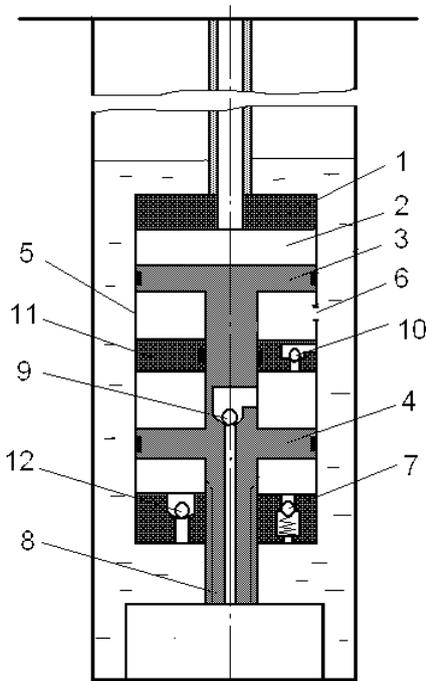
Усовершенствованный штанговый насос: 1 - верхний переходник; 2 - полость; 3,4 – поршни; 5 – корпус; 6 – отверстие; 7,9,10,12 - клапана; 8 - шлицевой вал; 11 -клапанная коробка
